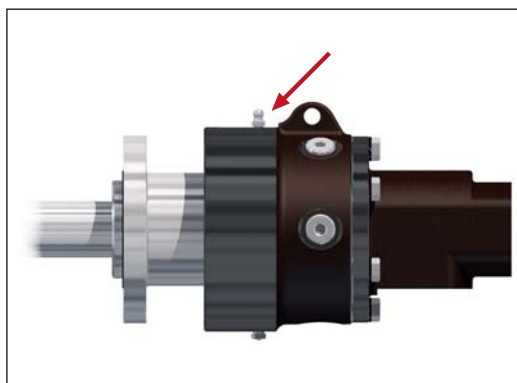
Utiliser un pistolet graisseur pour pour le graissage
